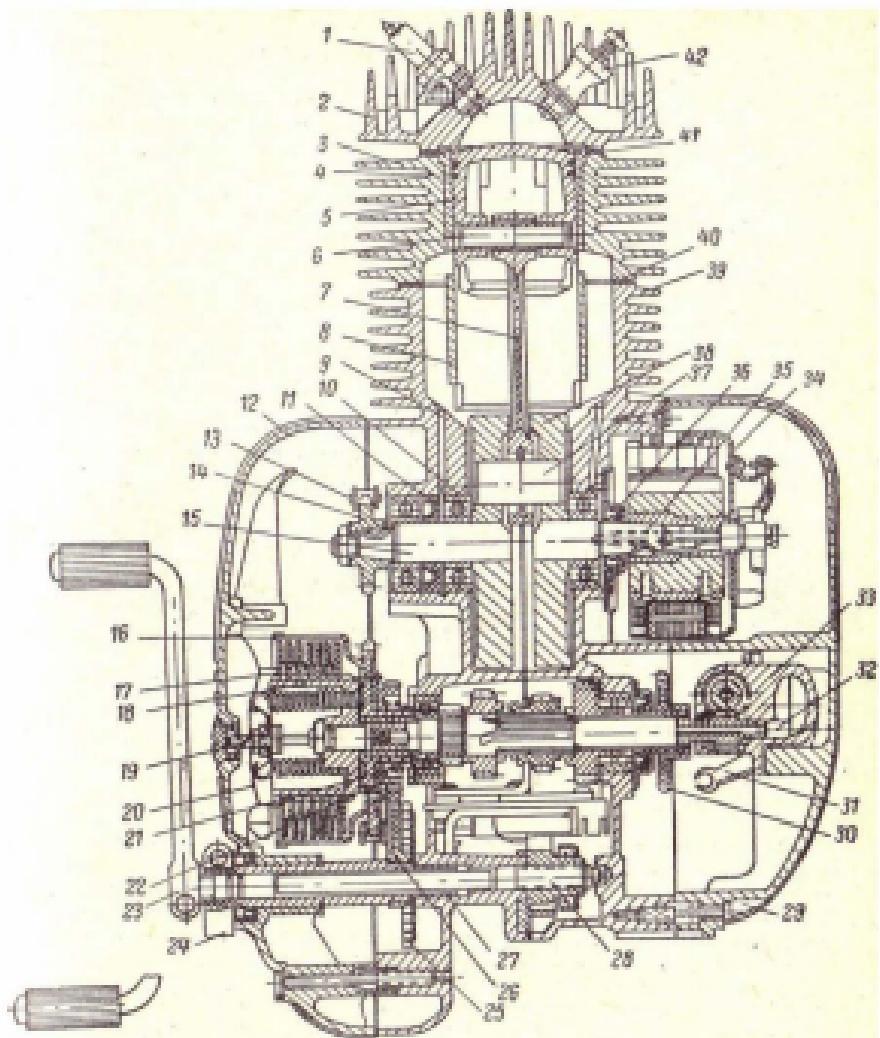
Блок двигателя с коробкой передач мотоцикла
